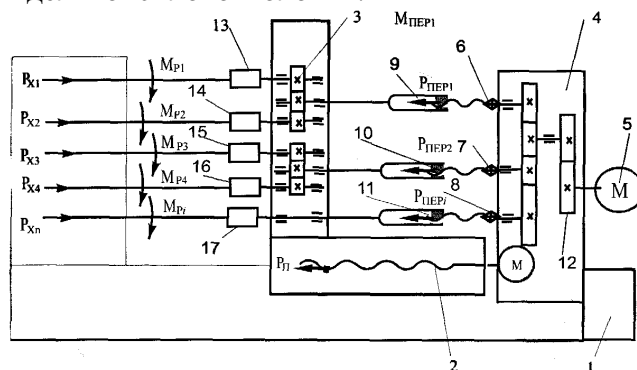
Силовa багатошпindelна головка з механізмом керування пружними деформаціями із загальною ланкою настроювання
